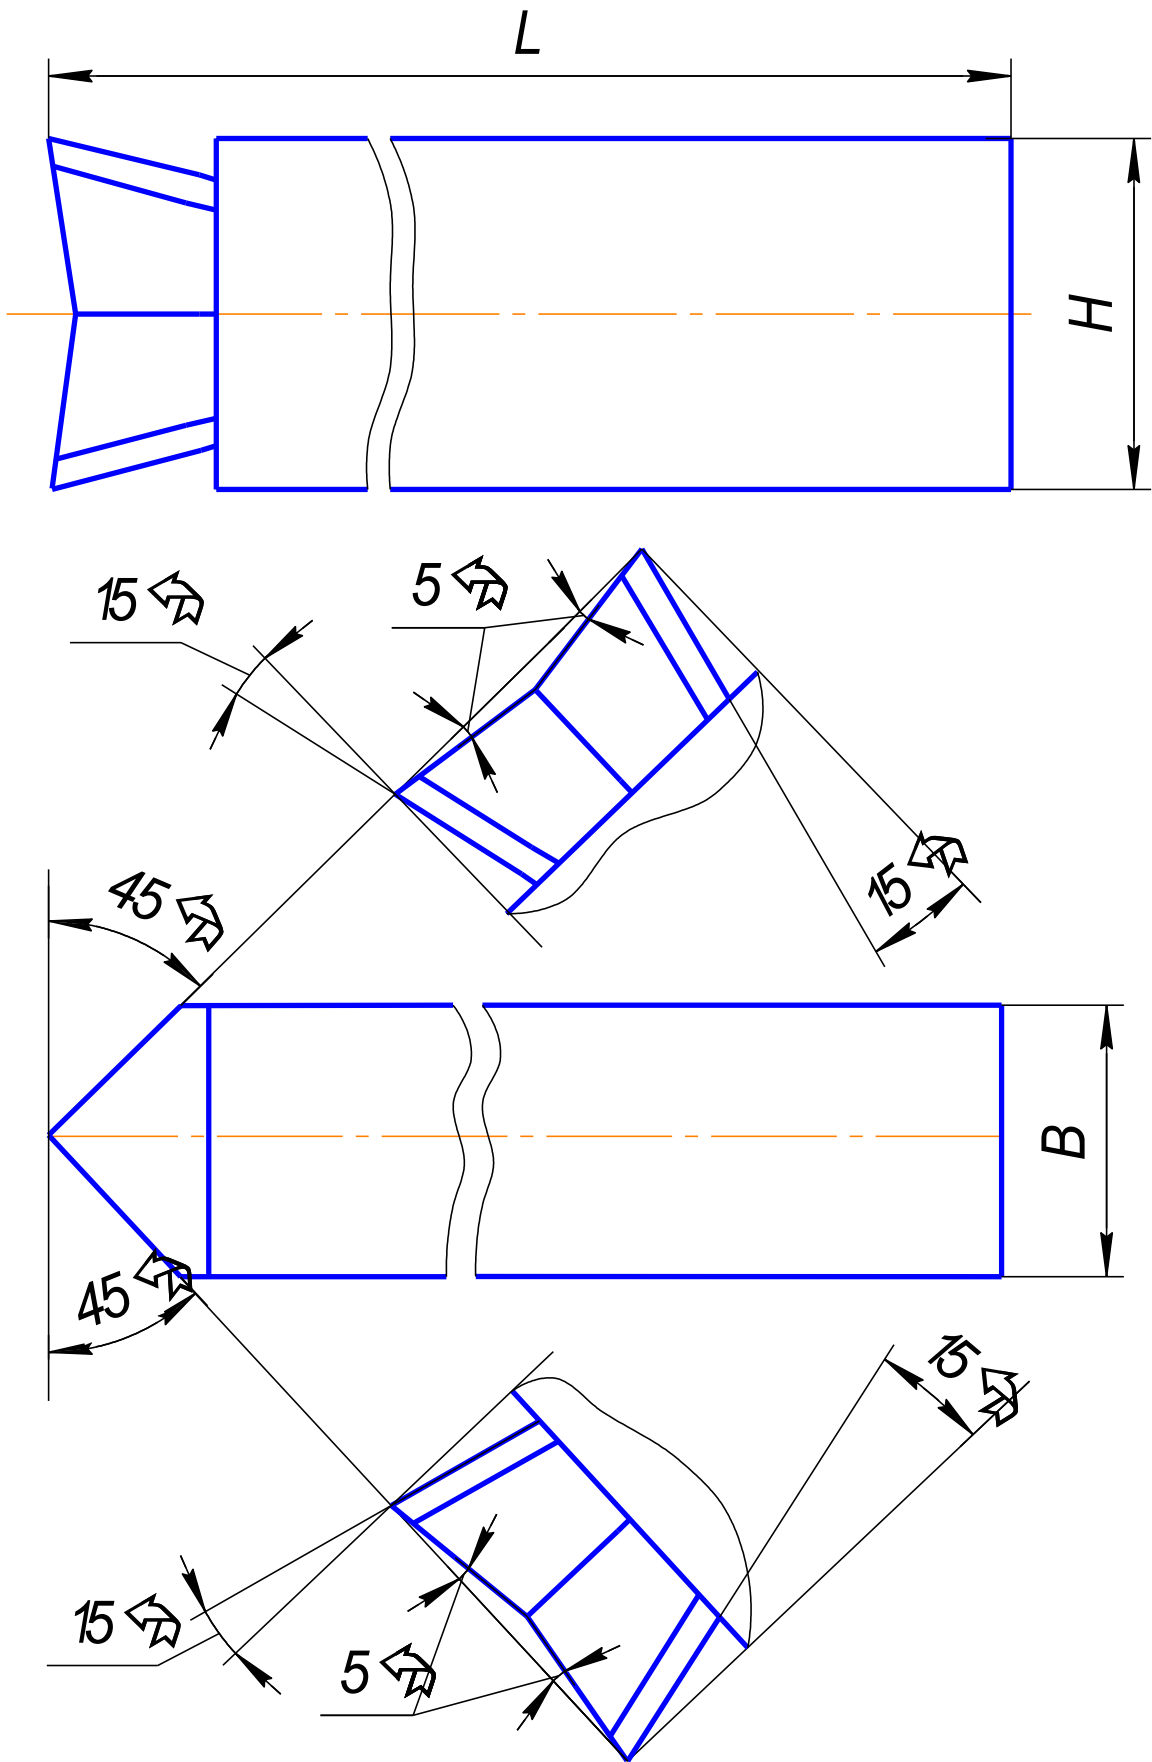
Різець стругальний прохідний прямий двовершинний
